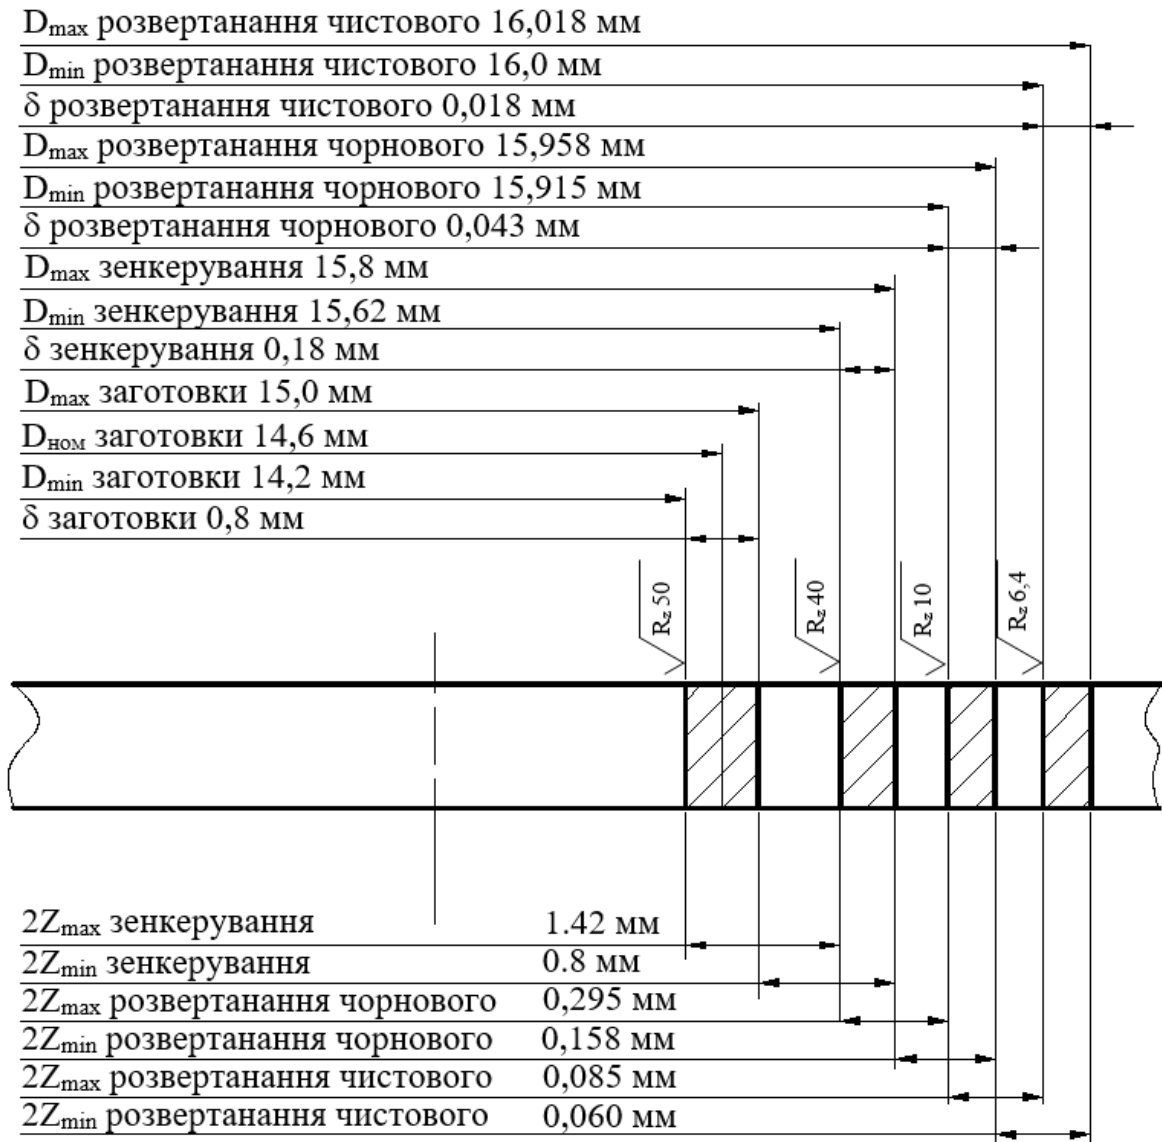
Схема розташування припусків на механічне оброблення
